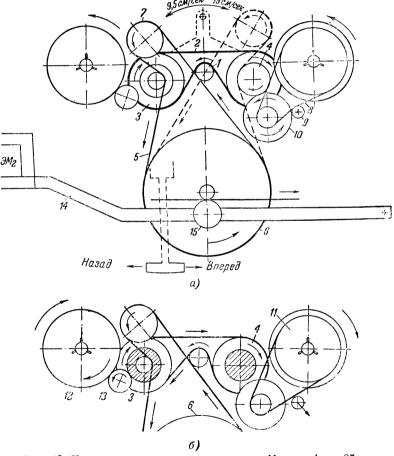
Кинематическая схема механизма «Магнитофона 85». a—рабочий ход; 6—ускоренная перемотка ленты.
